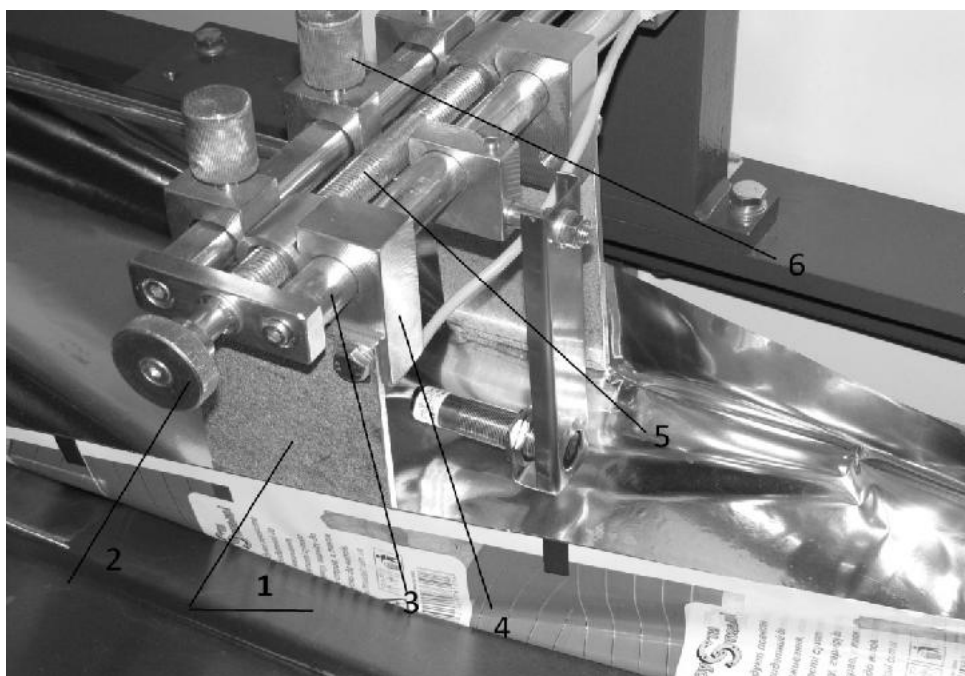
Схема формування горизонтального рукава для упаковки типу «флоу-пак»: 1- направляючі плити; 2- ручка регулювання; 3- направляючі корпусів; 4- корпуси плит; 5- гвинт; 6- шарніри
